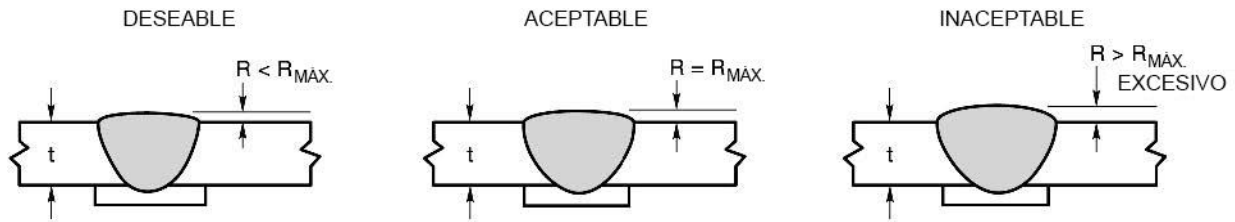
FIGURA A – REQUISITOS DE PERFILES DE SOLDADURA PARA JUNTA A TOPE (véase Tablas 2 y 3)
